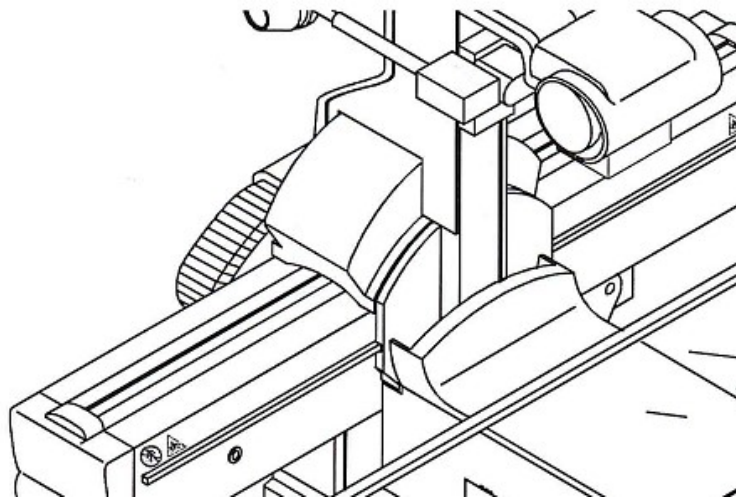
Обозначение зоны риска запрещающими знаками
